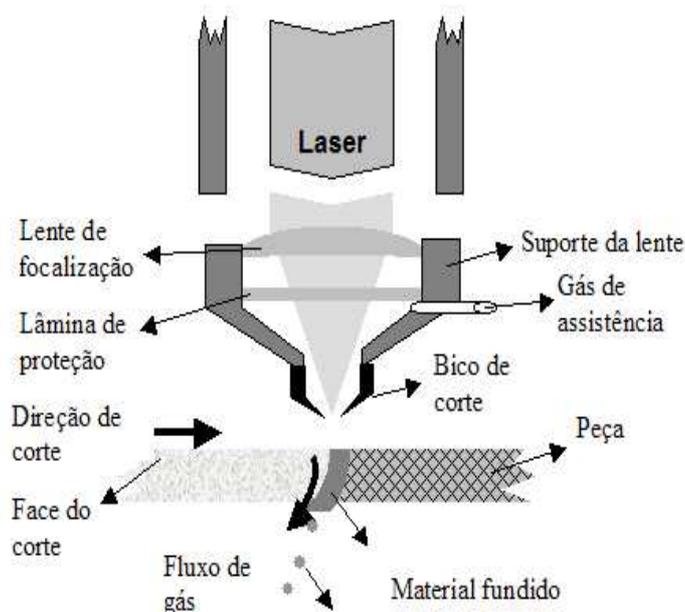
Cabeça de processamento laser e o mecanismo de corte.
